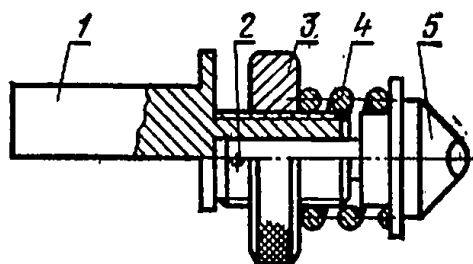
Малогабаритная державка для алмазного выглаживания:
